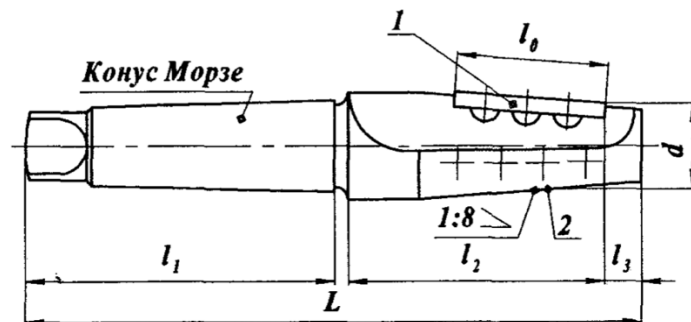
Однолезова конічна розвертка зі змінною твердосплавною пластиною
